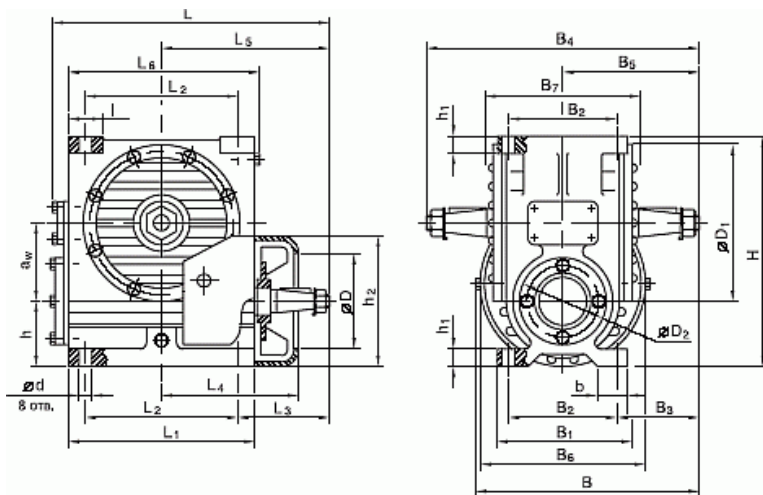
Редуктор черв'ячний типу ЧГ-125
